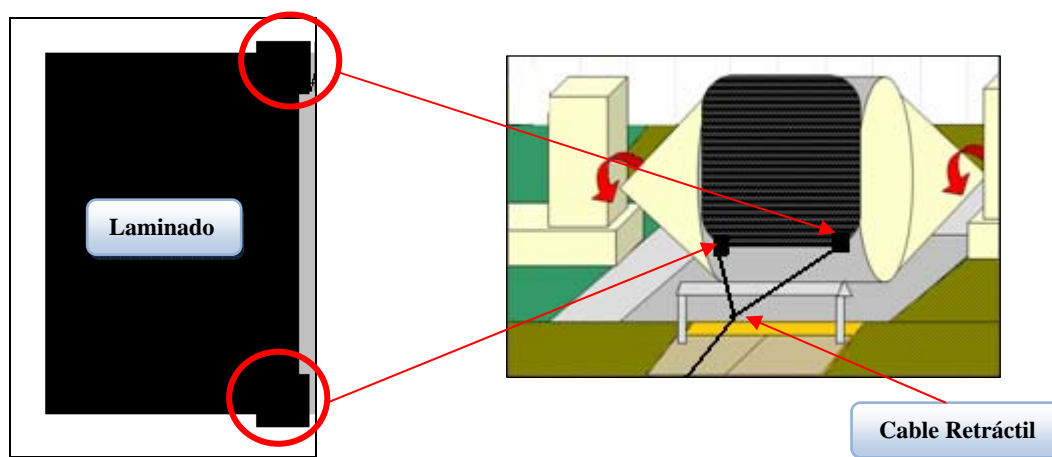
y 326. PASO 2: Posicionadores de Laminado y Cable Retráctil
